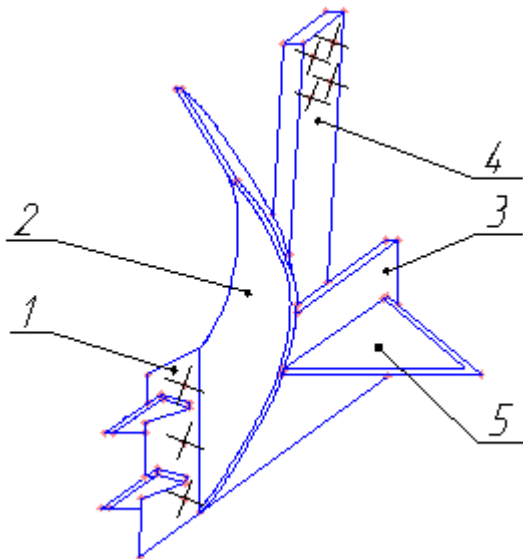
Корпус плуга: 1 – леміш; 2 – полиця; 3 – польова дошка; 4 – стояк; 5 – горизонтальний ніж
